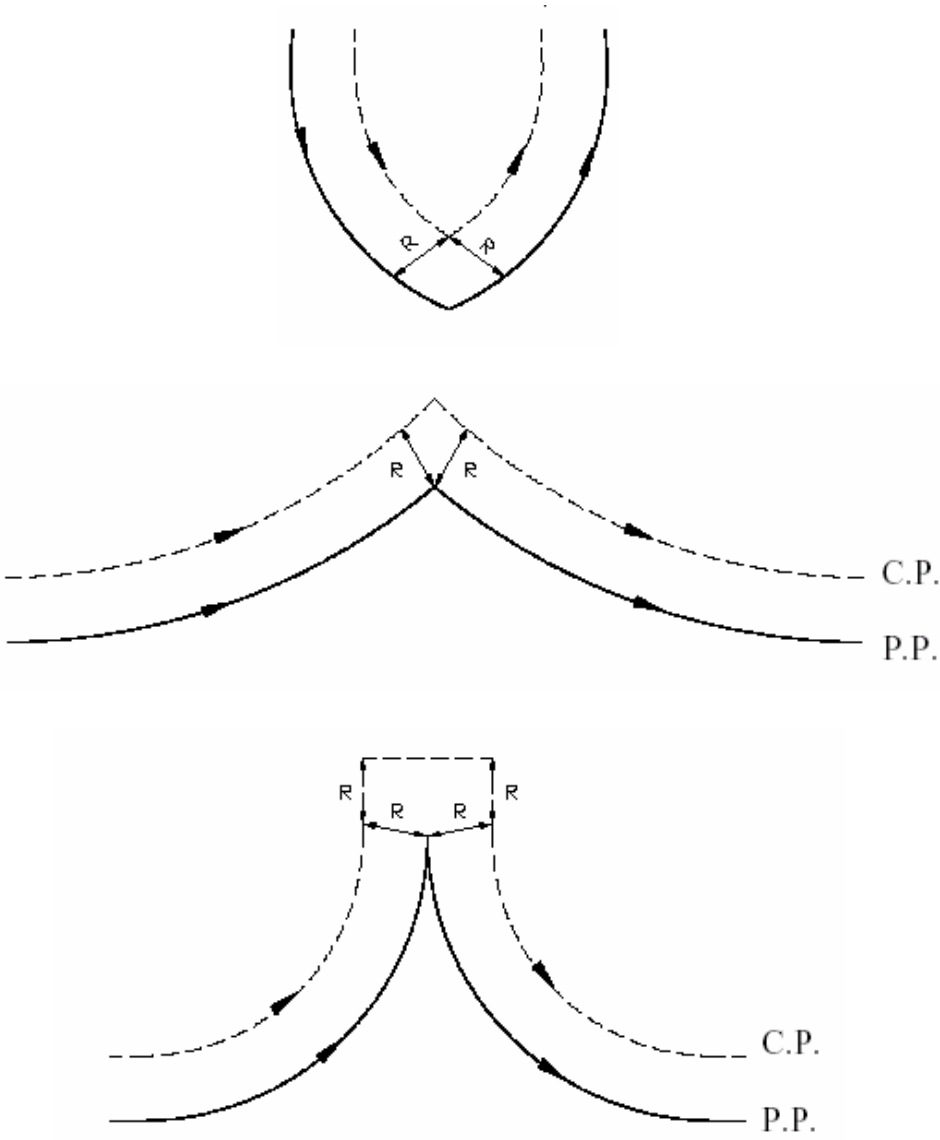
27 (3) 刀具半径补偿的刀具轨迹
